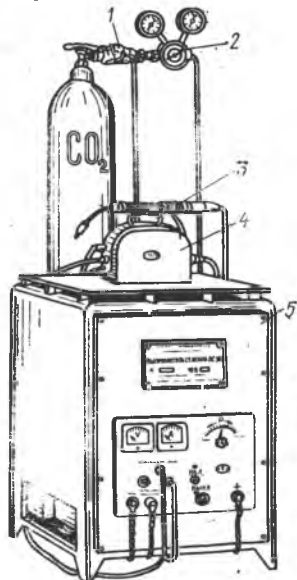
Общий вид сварочного полуавтомата А-547У:
